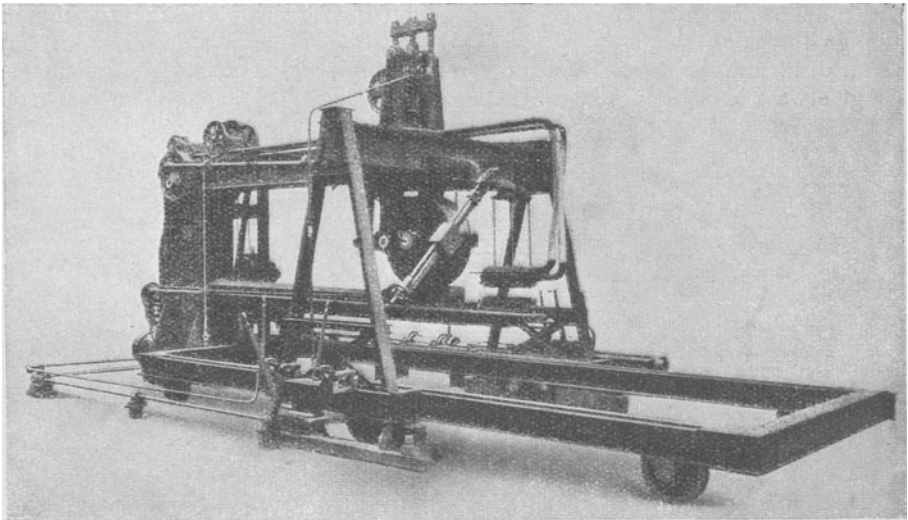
Wassergas-Rollenschweißmaschine.
